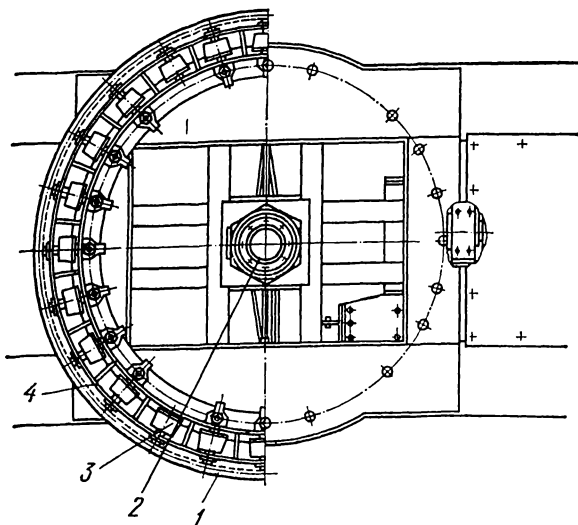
Опорно-поворотное устройство многокаткового типа:
